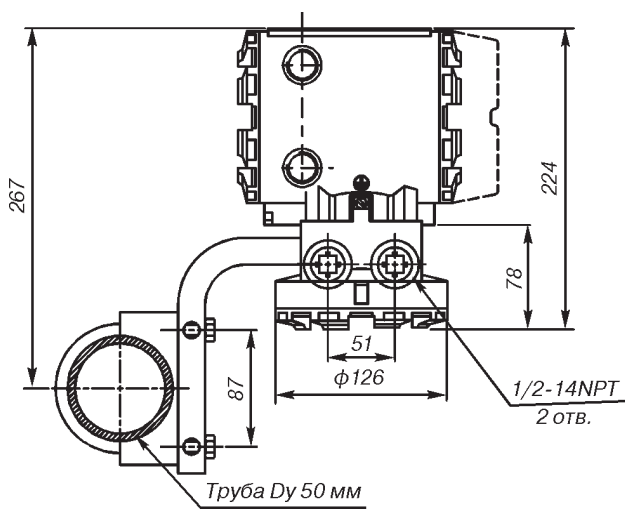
Габаритные и присоединительные размеры преобразователя 8732Е, удаленный монтаж на трубе Ду 50.
